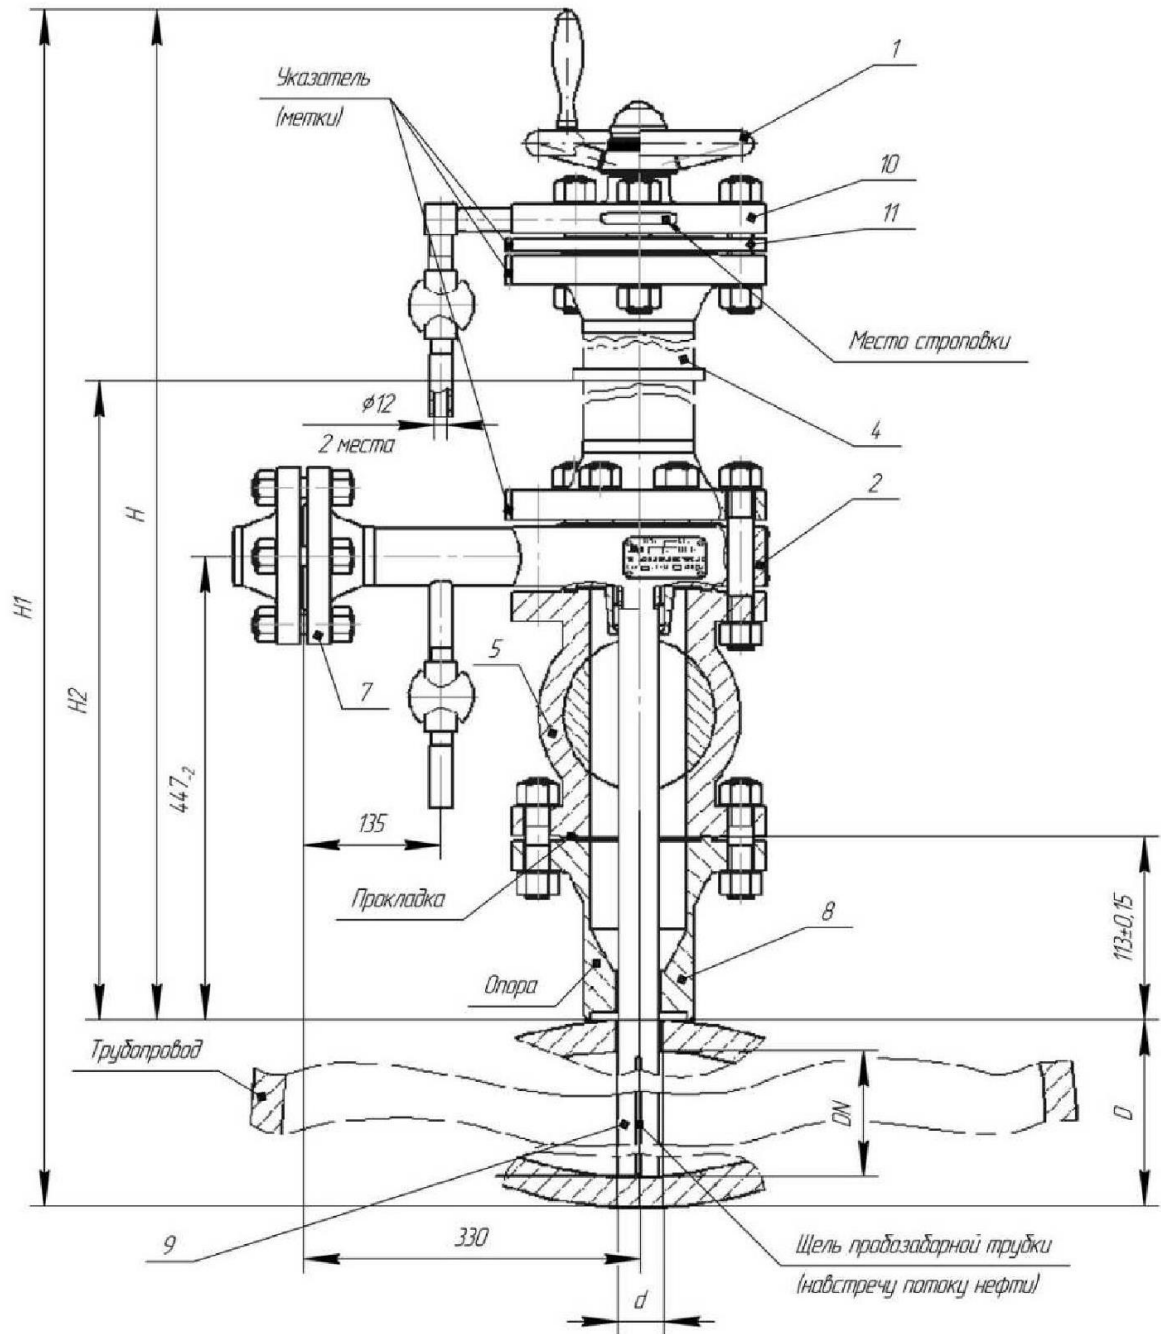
Конструкция устройства пробозабортного щелевого типа с лубрикатром
